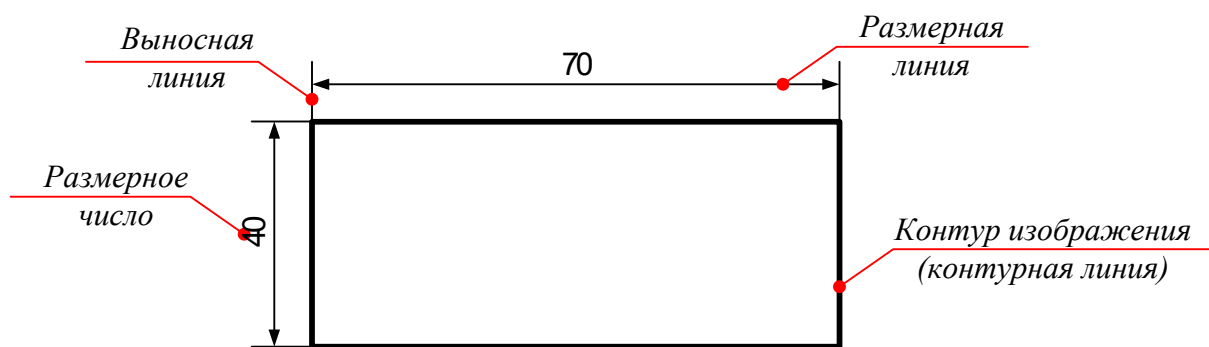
Выносные и размерные линии с размерным числом на чертежах
